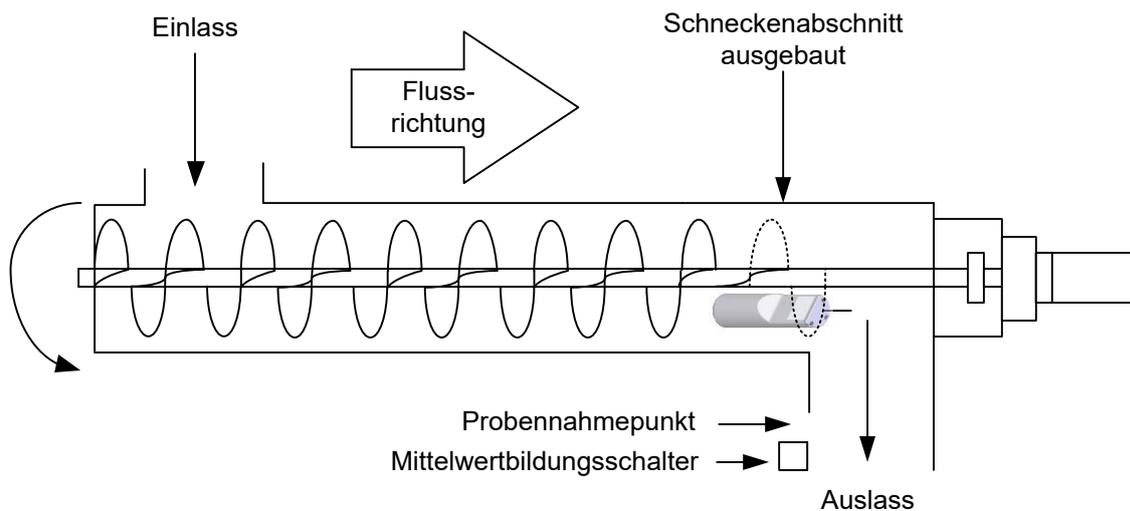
Montage des Hydro-Probe in einem Schneckenförderer
